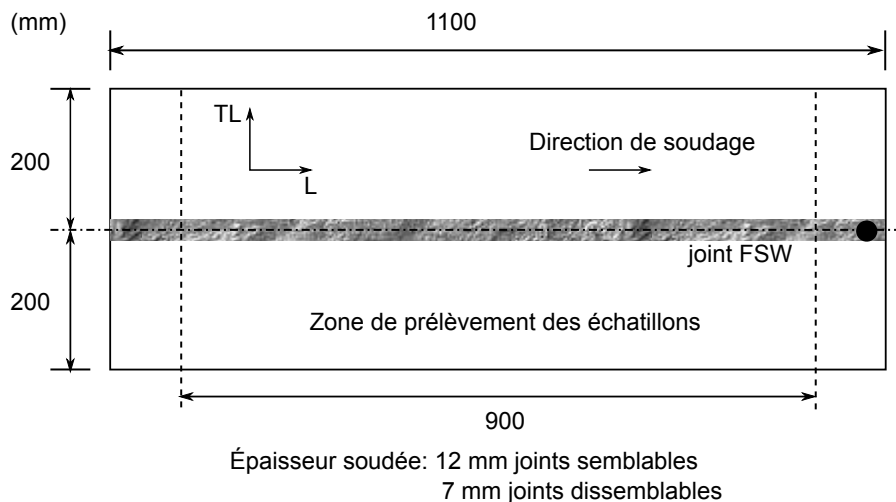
Zone de prélèvement des échantillons dans les plaques soudées par FSW
